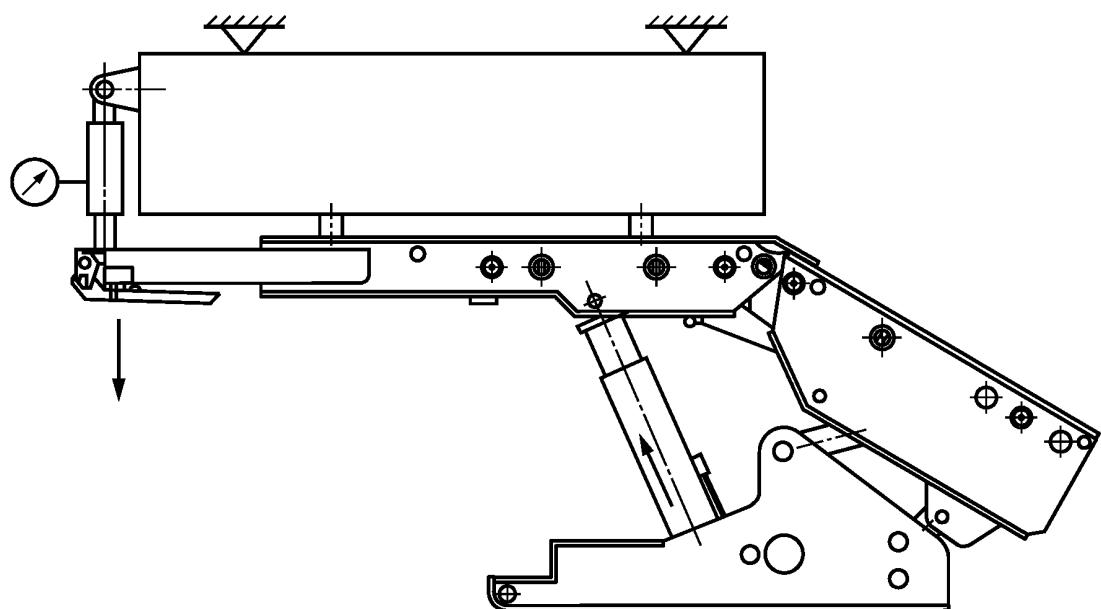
Схема нагружения для определения сопротивления на конце передней консоли жесткого перекрытия пенального типа
